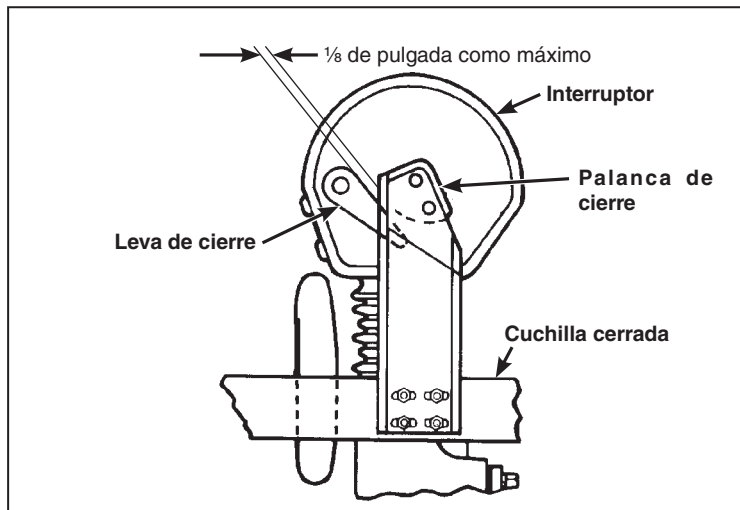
El ensamble de las cuchillas en posición totalmente Cerrada.
